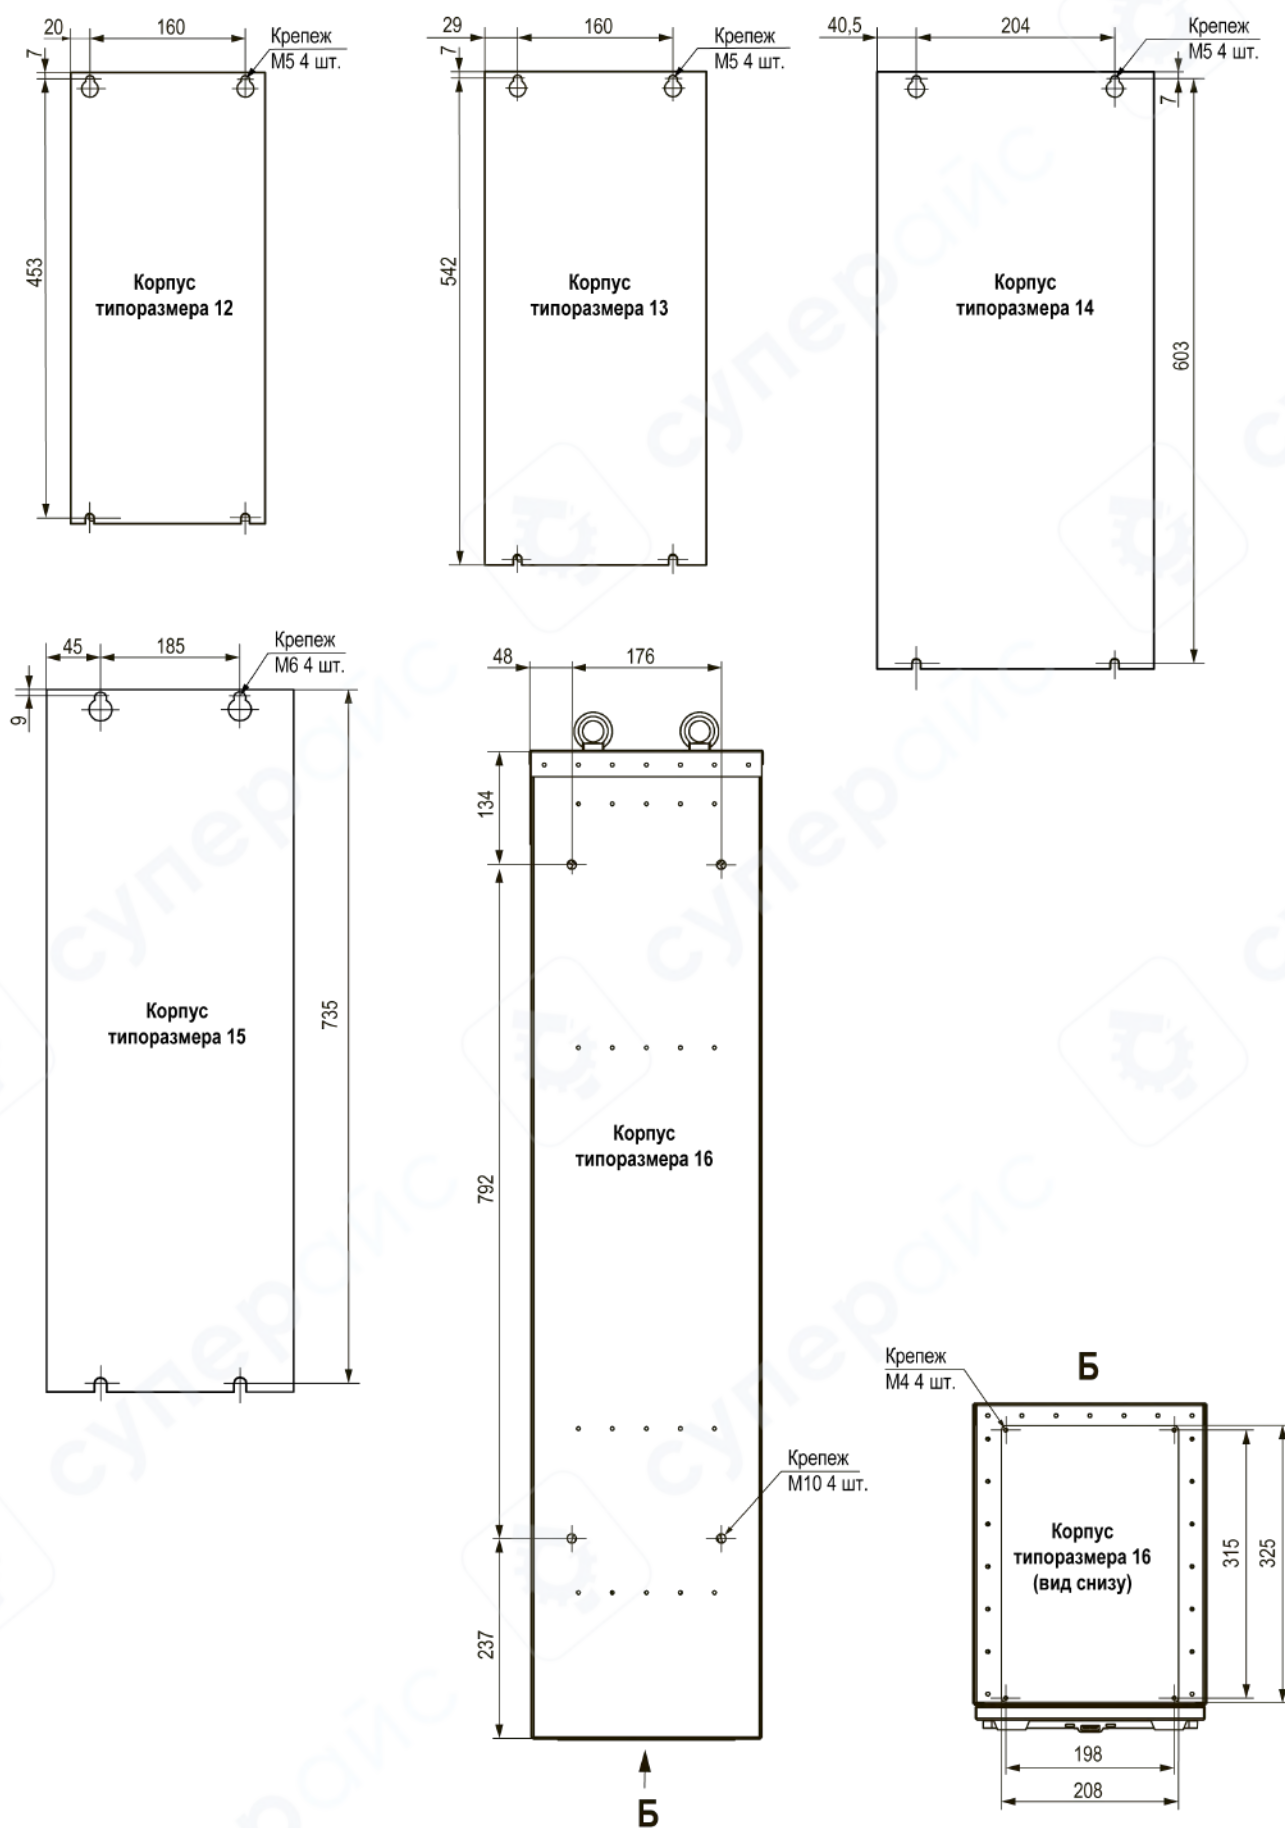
Присоединительные размеры для корпусов типоразмеров 12–16
